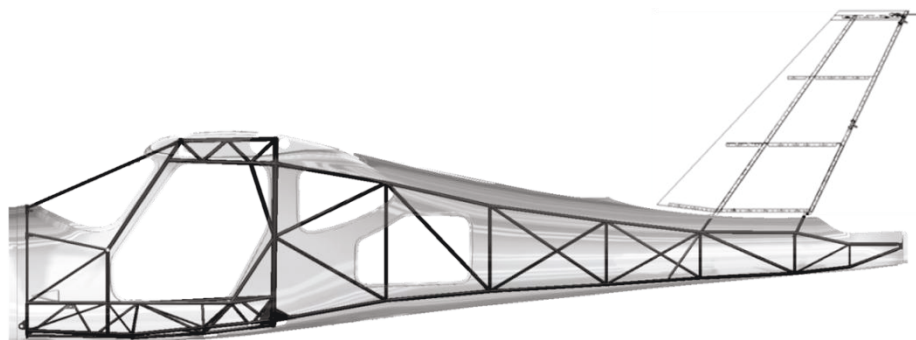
Assemblage pour la fabrication des moules principaux du fuselage
